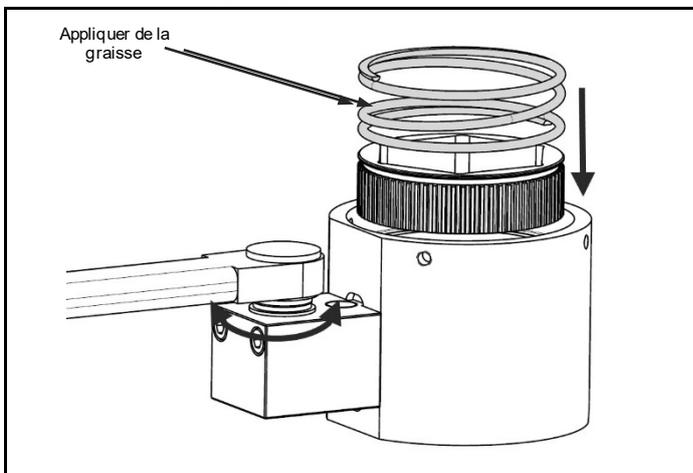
Appliquer de la graisse et introduire la douille à engrenage, suivie des ressorts de compression
